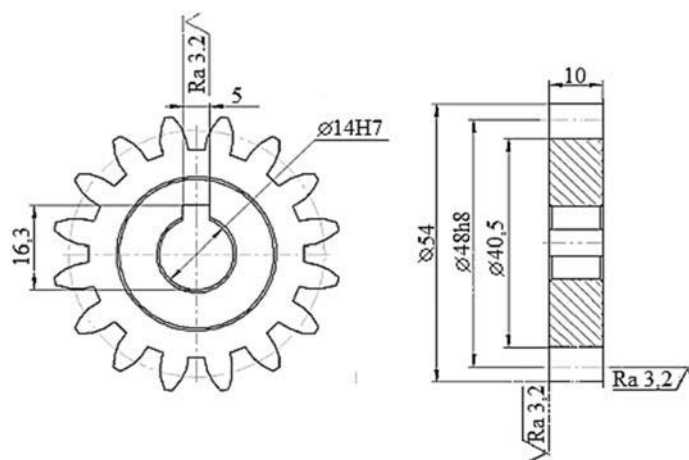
Деталь «Цилиндрическое зубчатое колесо»
